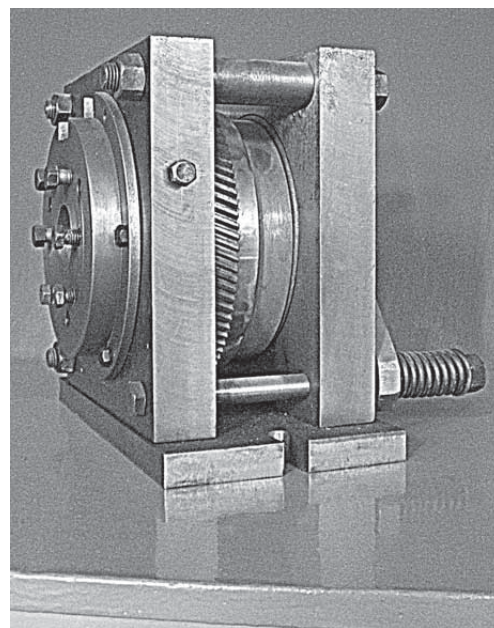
Экспериментальный образец обкатника с промежуточными опорными катками
